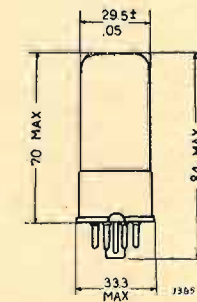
Dimensioni di ingombro della valvola 6J5 GT.
